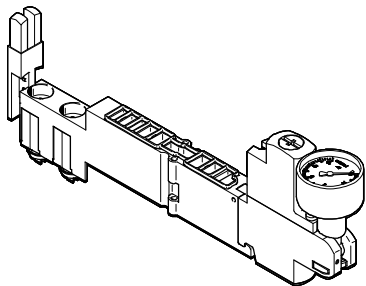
Druckreglerplatte, Typ VMPA...B8-R...C2-C-... mit optionalem Manometer
